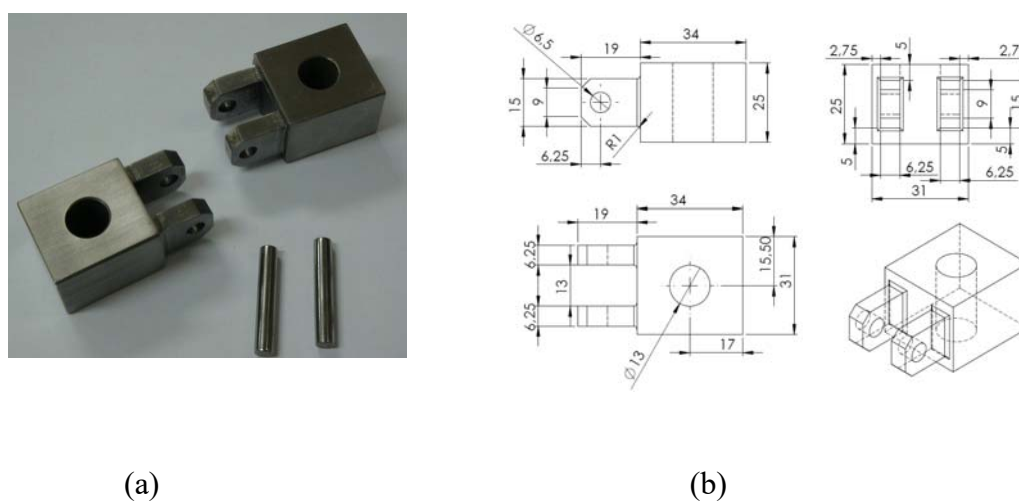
Dispositivo de fixação (*loading clevis*): a) dispositivo fabricado; b) dimensões do dispositivo.
